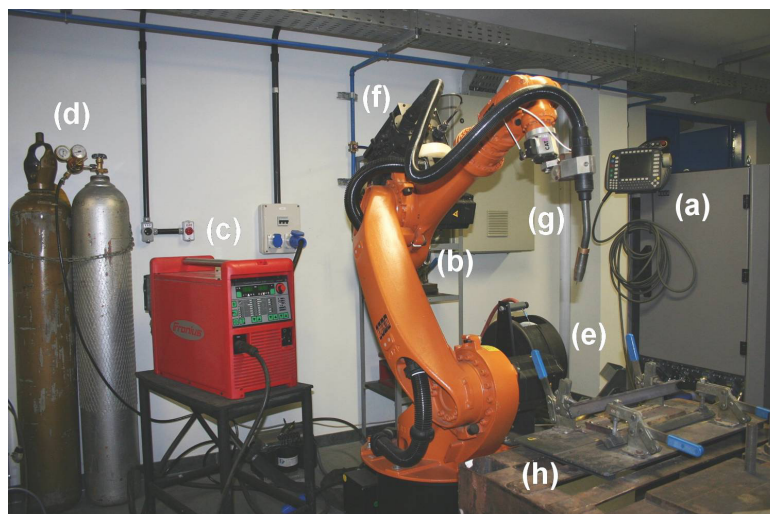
Célula robótica de soldagem. (a) Painel de controle do robô manipulador; (b) Robô manipulador da Soldagem; (c) fonte de soldagem; (d) cilindro de gás; (e) rolo de arame; (f) alimentador de arame; (g) tocha de soldagem e (h) mesa de soldagem com grampos de fixação.
